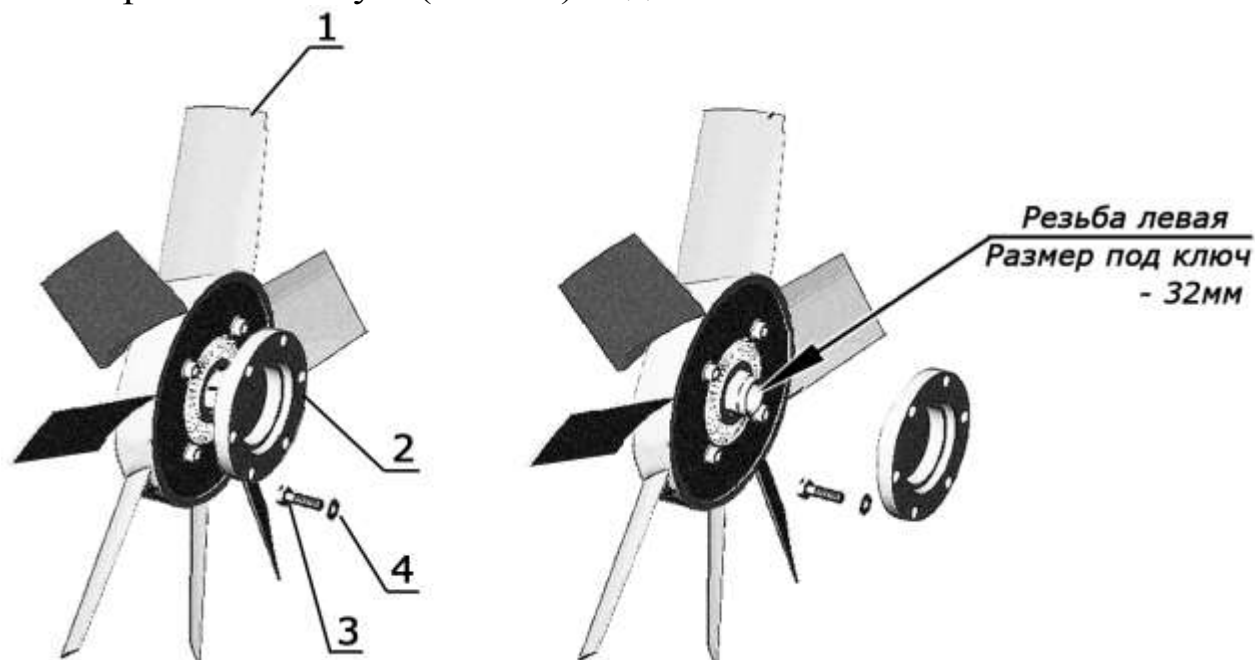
Привод вентилятора: 1 – вентилятор с автоматической вязкостной муфтой привода; 2 – проставка; 3 – болт; 4 – шайба
